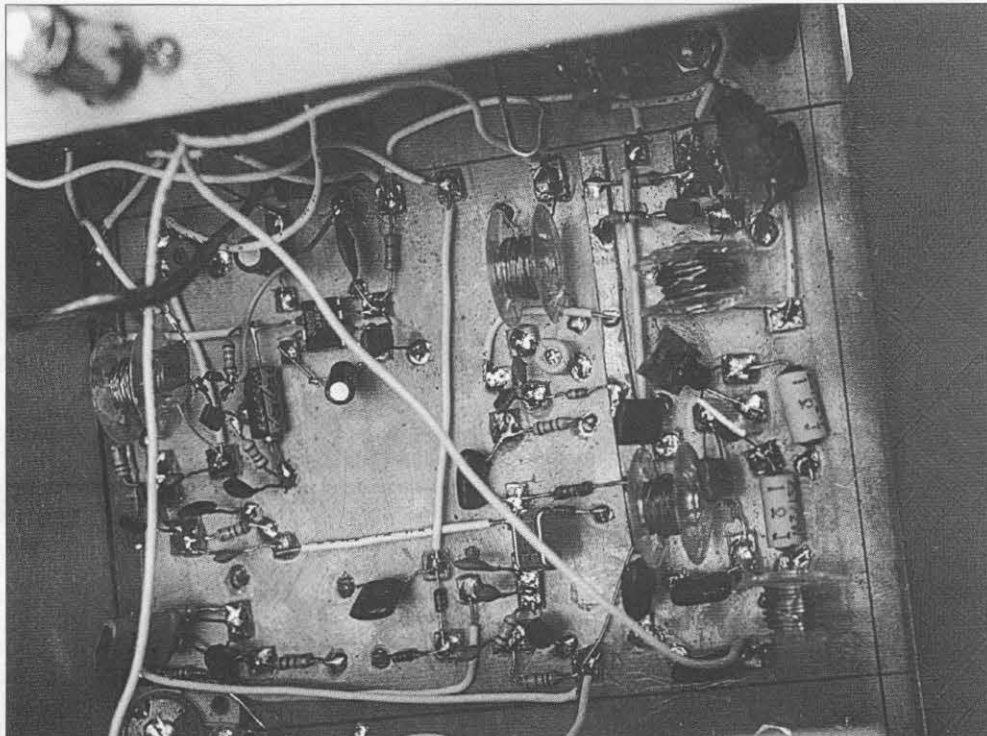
Foto D. Las inductancias están construidas sobre bobinas de plástico muy baratas diseñadas para las máquinas de coser Singer. Vea el texto para más detalles.
